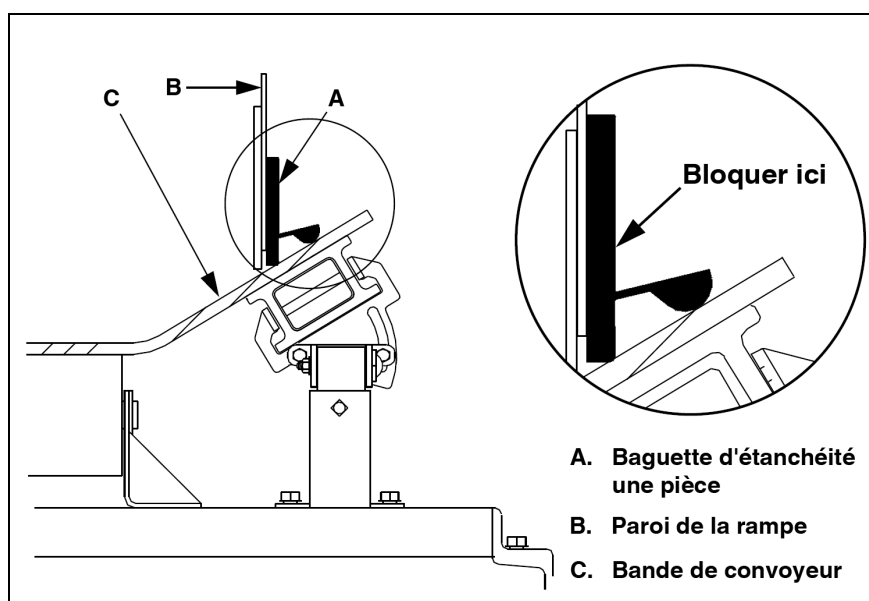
Installation de la baguette d'étanchéité une pièce en caoutchouc
